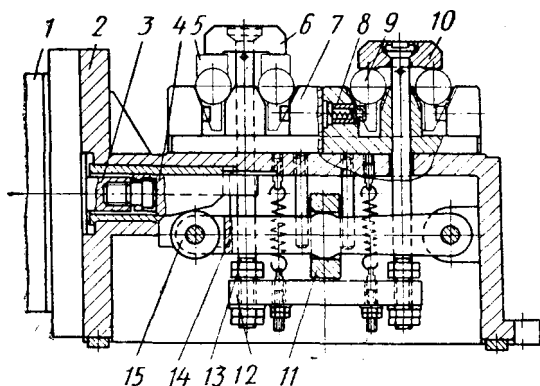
Двухрядное восьмиместное фрезерное приспособление с зажимом от одного пневмоцилиндра
